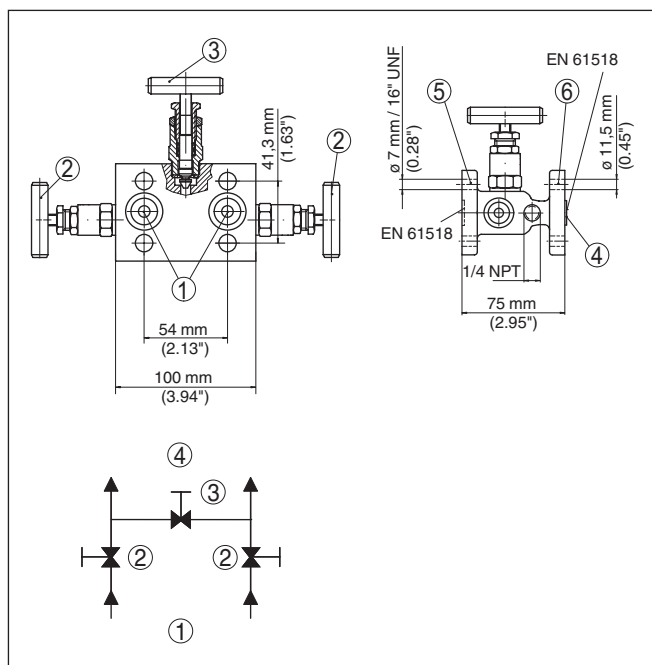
Конструкция 3-вентильного блока по EN 61518
